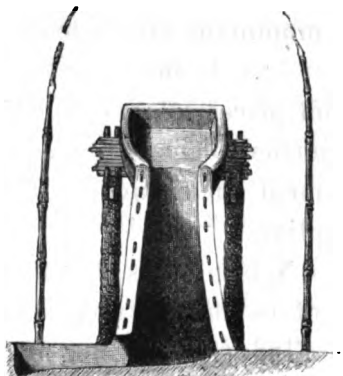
Coupe verticale suivant la ligne a b du plan.
